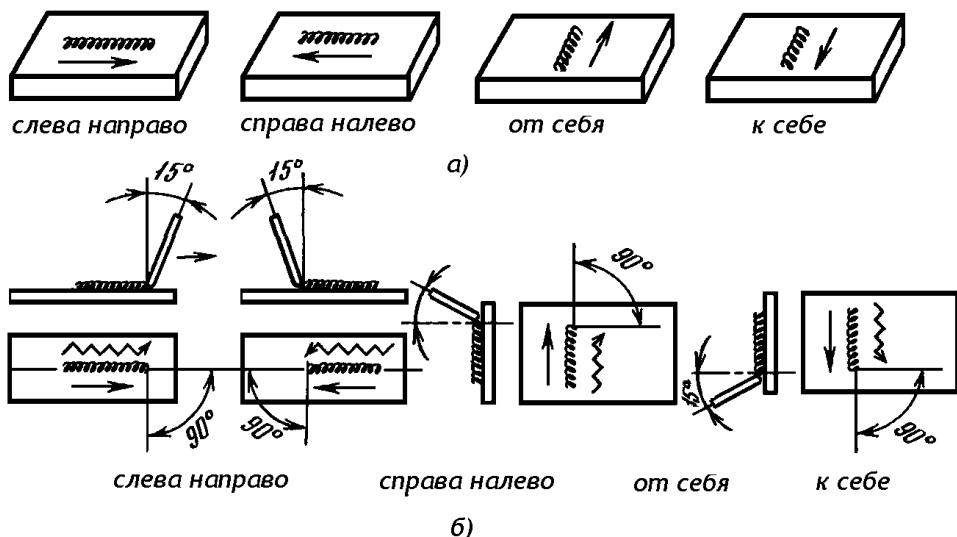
Направления сварки (а) и наклон электрода (б)
